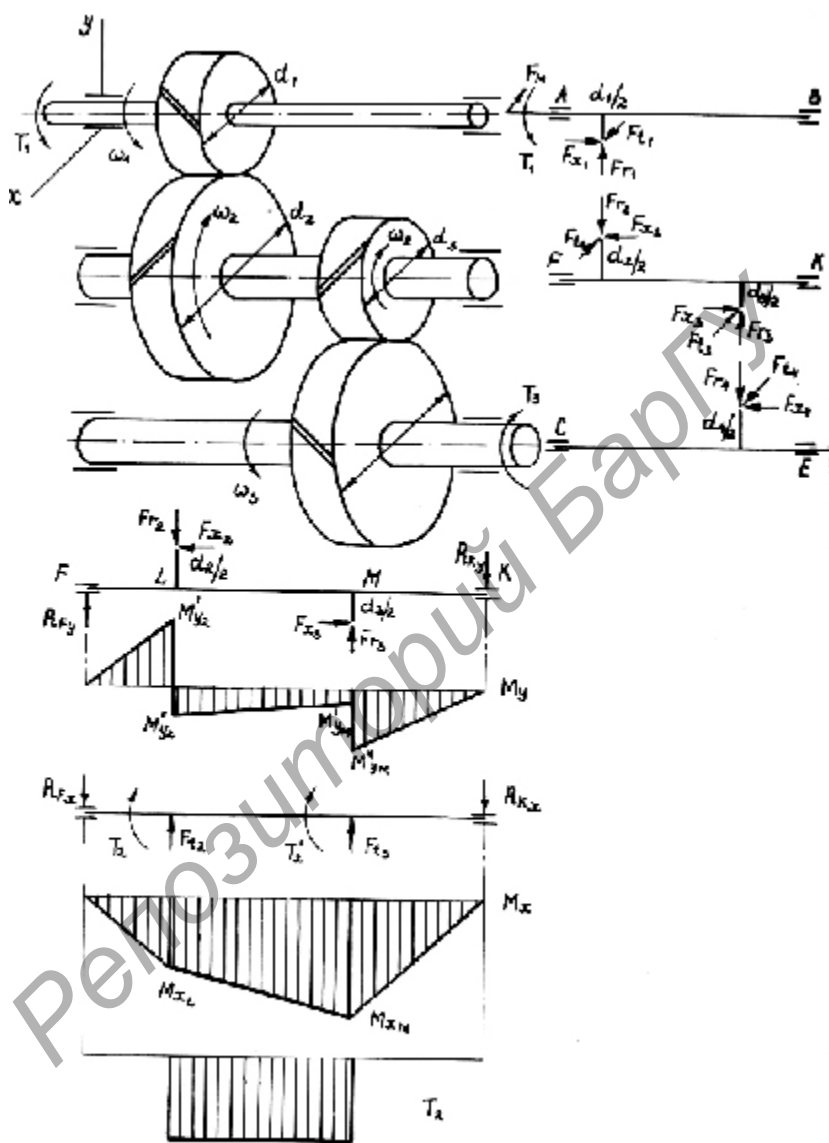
Цилиндрическая косозубая двухступенчатая развернутая передача
